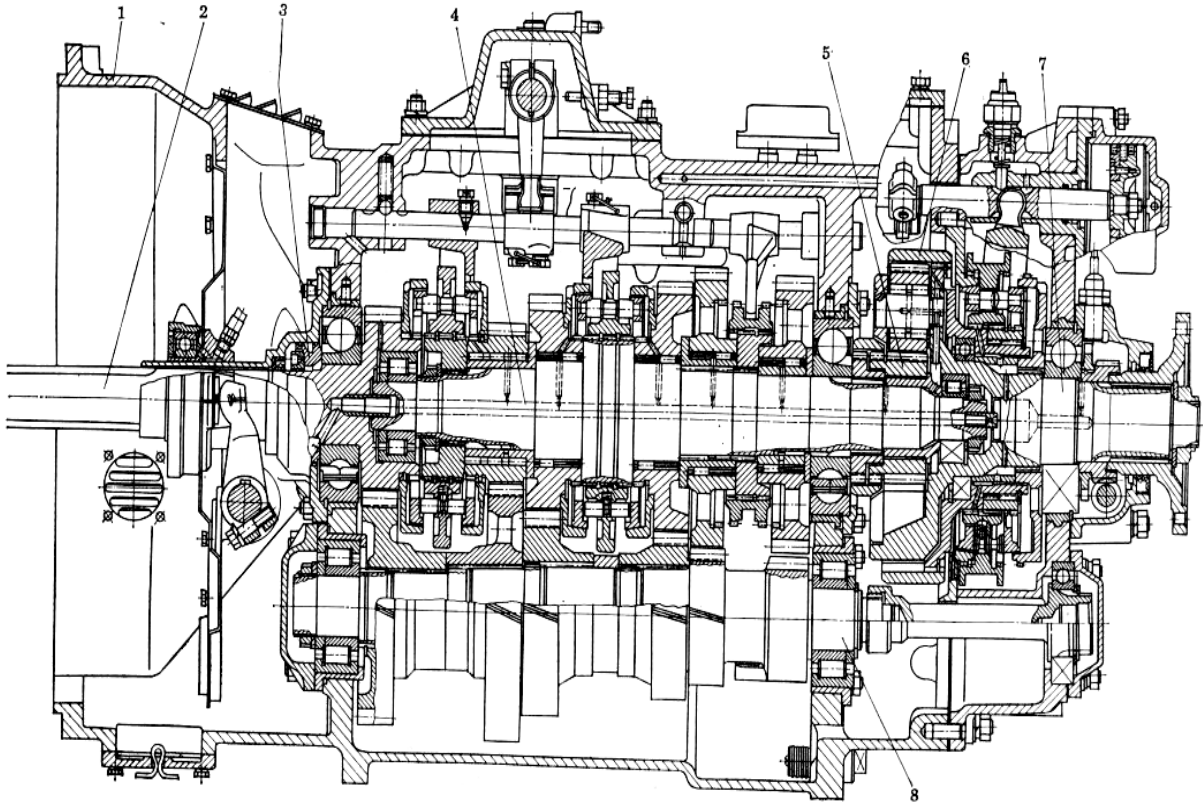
Конструкция девятиступенчатой коробки передач
